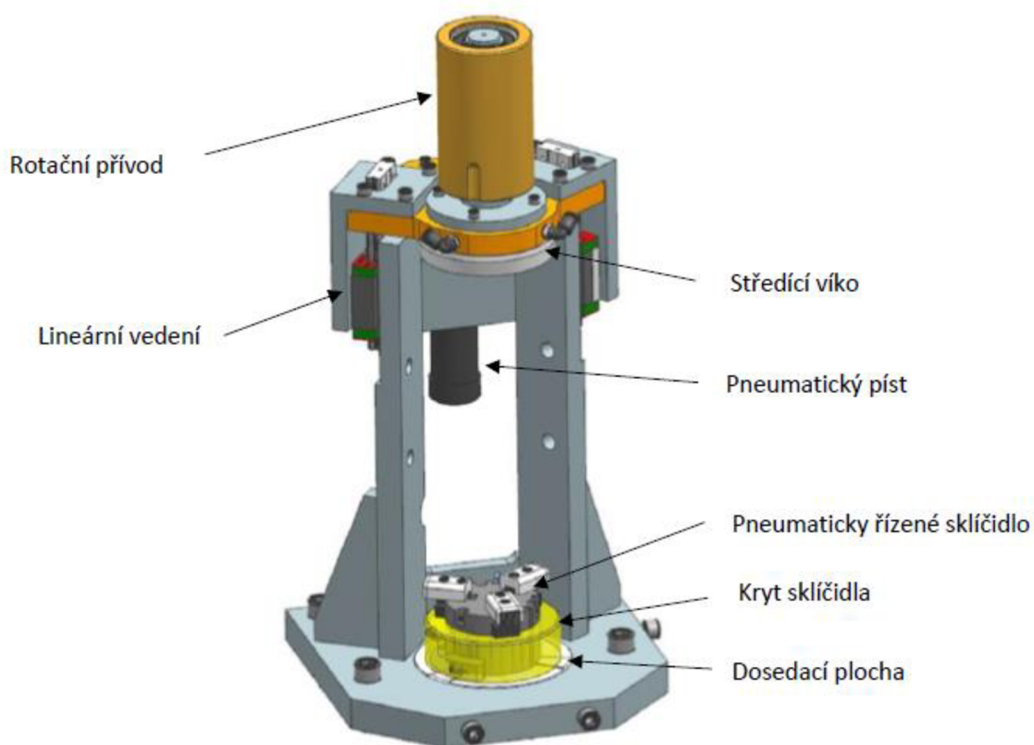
Upnutí polotovaru v přípravku pro hrubování [3]
